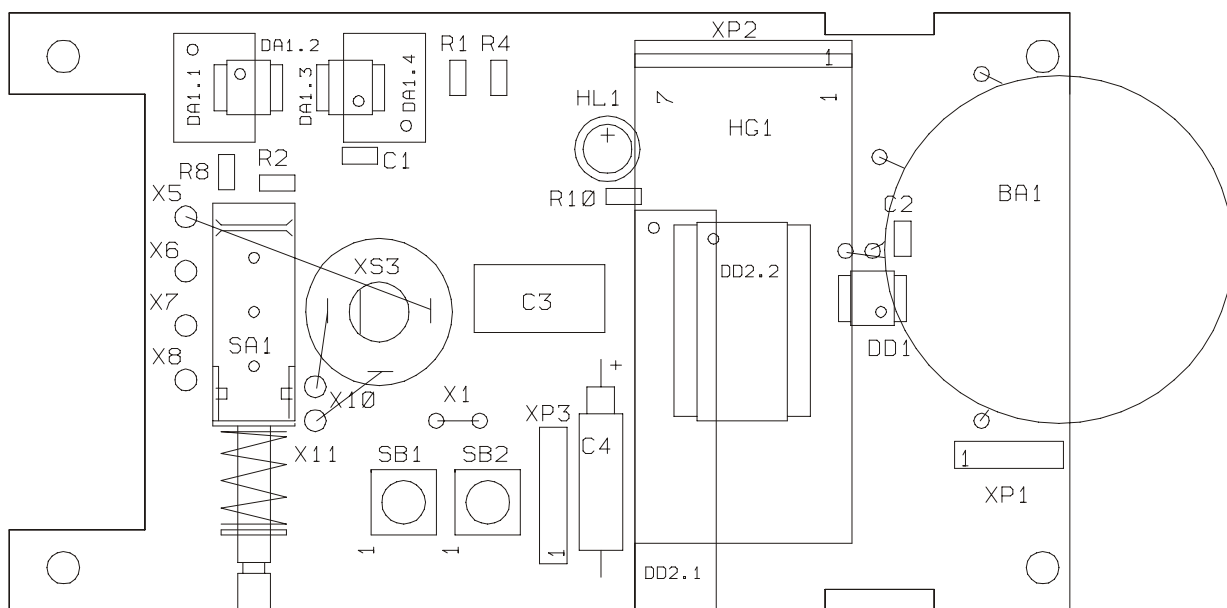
Сборочный чертеж платы обработки ФП11.3. Сторона монтажа.
